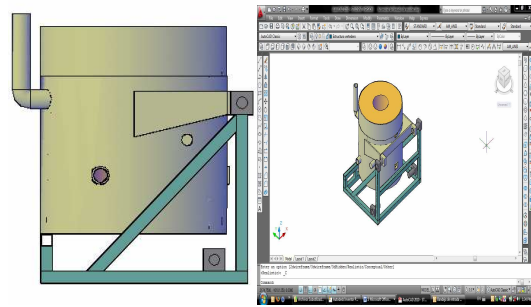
Imagen de sistema horno – estructura, vista frontal e isométrica.
